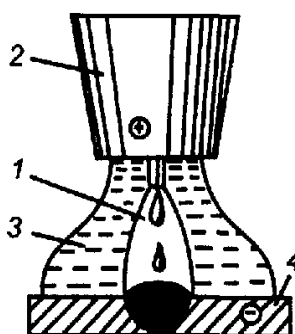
Схема механизированной сварки в защитных газах
